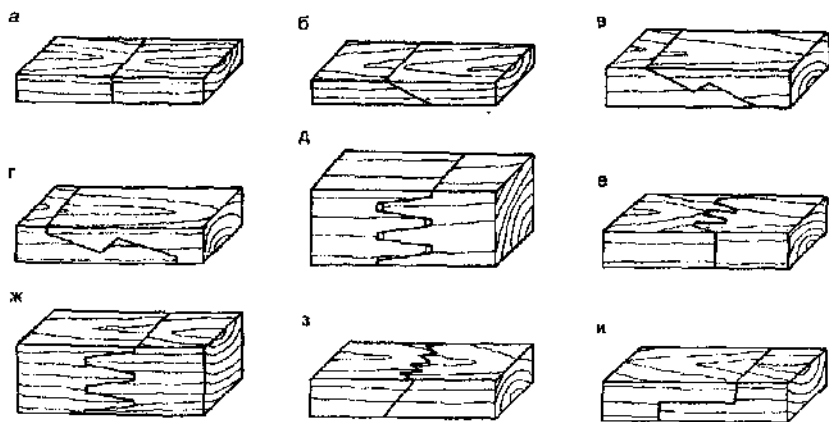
Клеевые соединения брусьев и досок по длине: а — торцовое; б — на «ус»; в — на ступенчатый «ус»; г — на ступенчатый «ус» с затуплением; д — зубчатое; е — вертикальное зубчатое; ж — горизонтальное зубчатое; з — зубчатое на «ус»; и — ступенчатое
